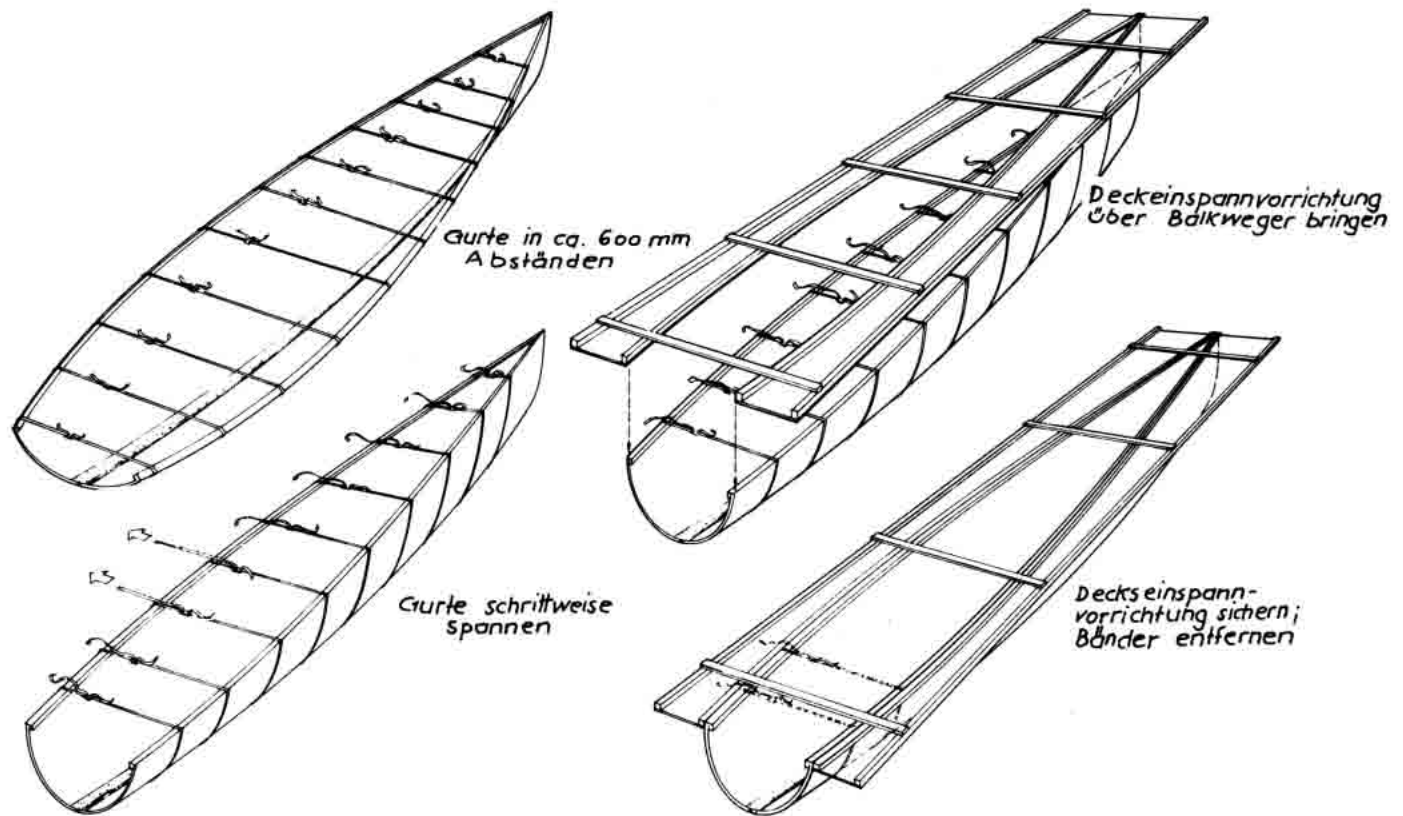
Einbiegen mit Plastik-Bändern oder -Gurten.
